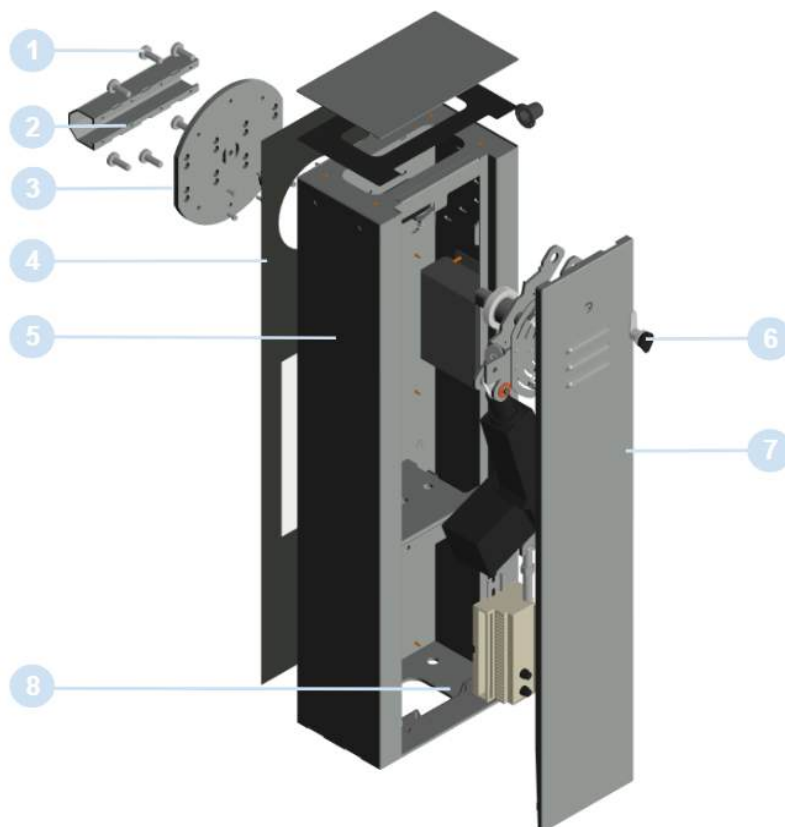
Внешний вид и состав корпуса шлагбаума
